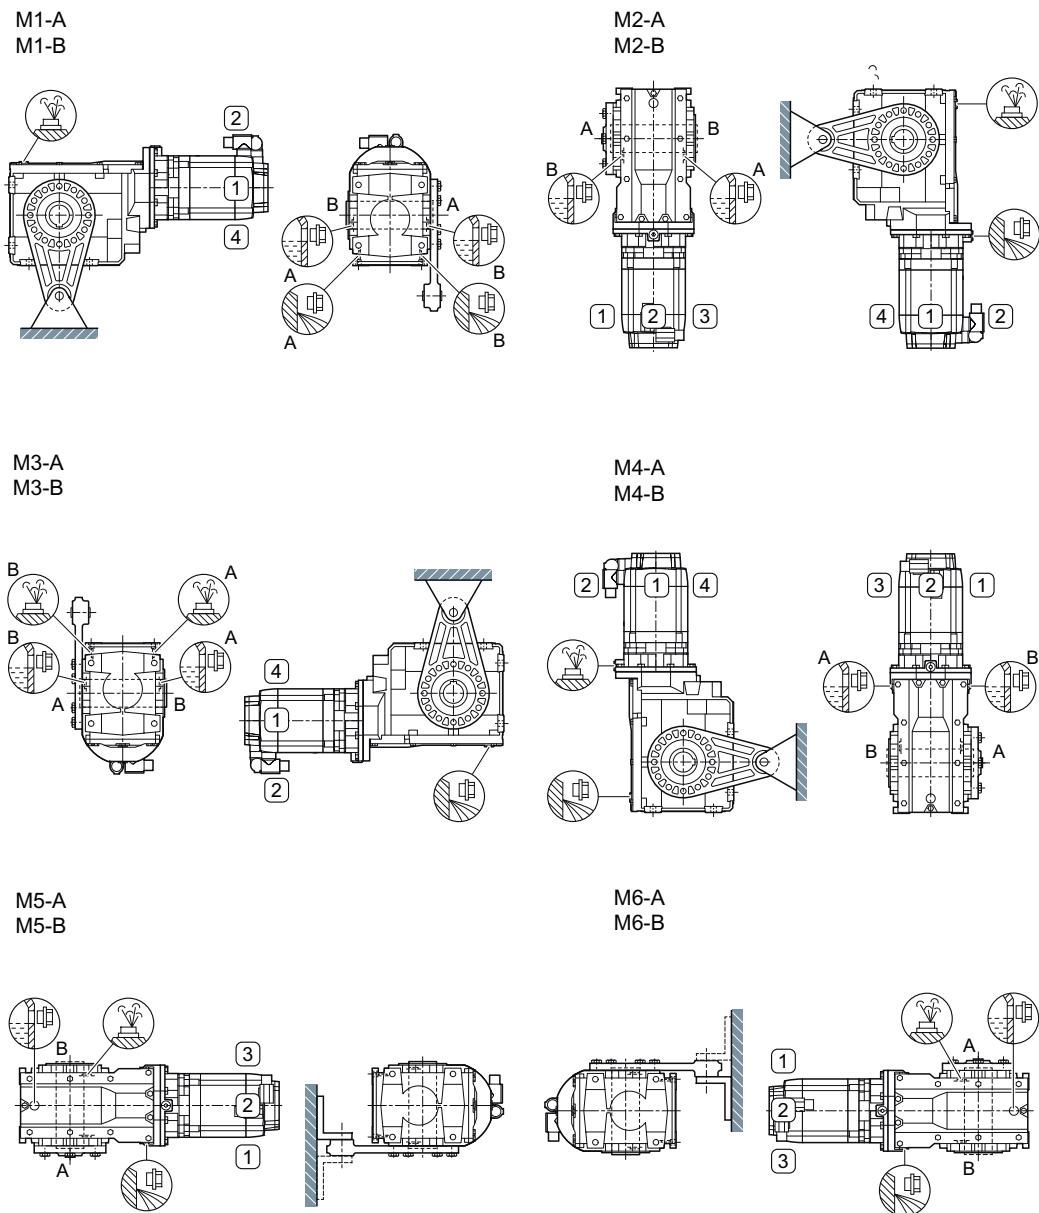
Einbaulagen für Servo-Kegelradgetriebemotor BAD, Aufsteckausführung, Baugrößen 39 - 49, 2-stufig
